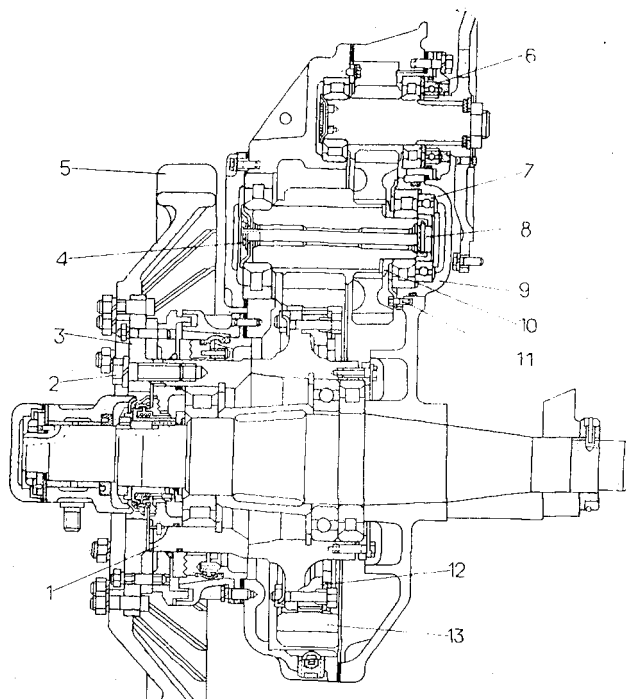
Бортовой редуктор с передаточным числом 14, 79:
